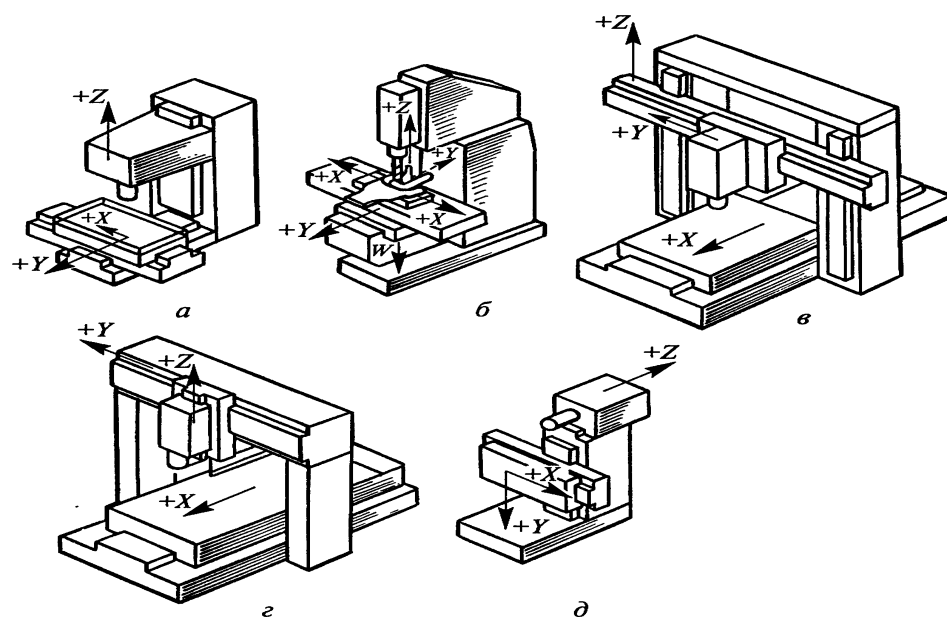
Компоновочні схеми фрезерних верстатів з ЧПК з позначенням осей координат X, Y, Z і W:
